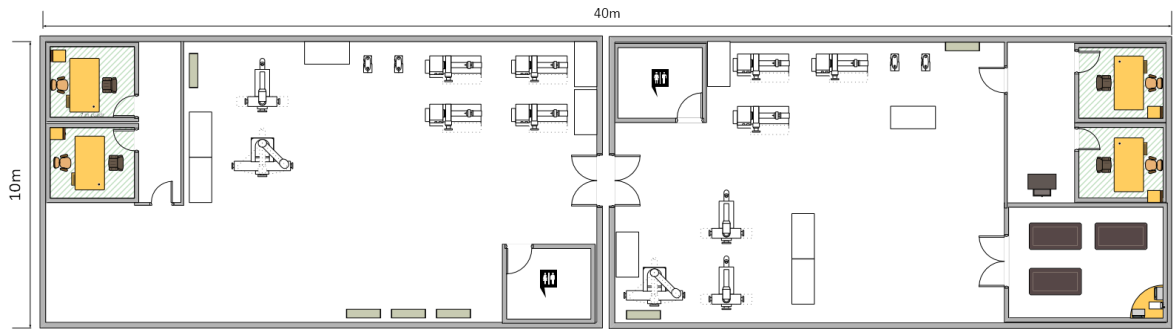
Layout de planta extendida. Fuente: Elaboración propia.
